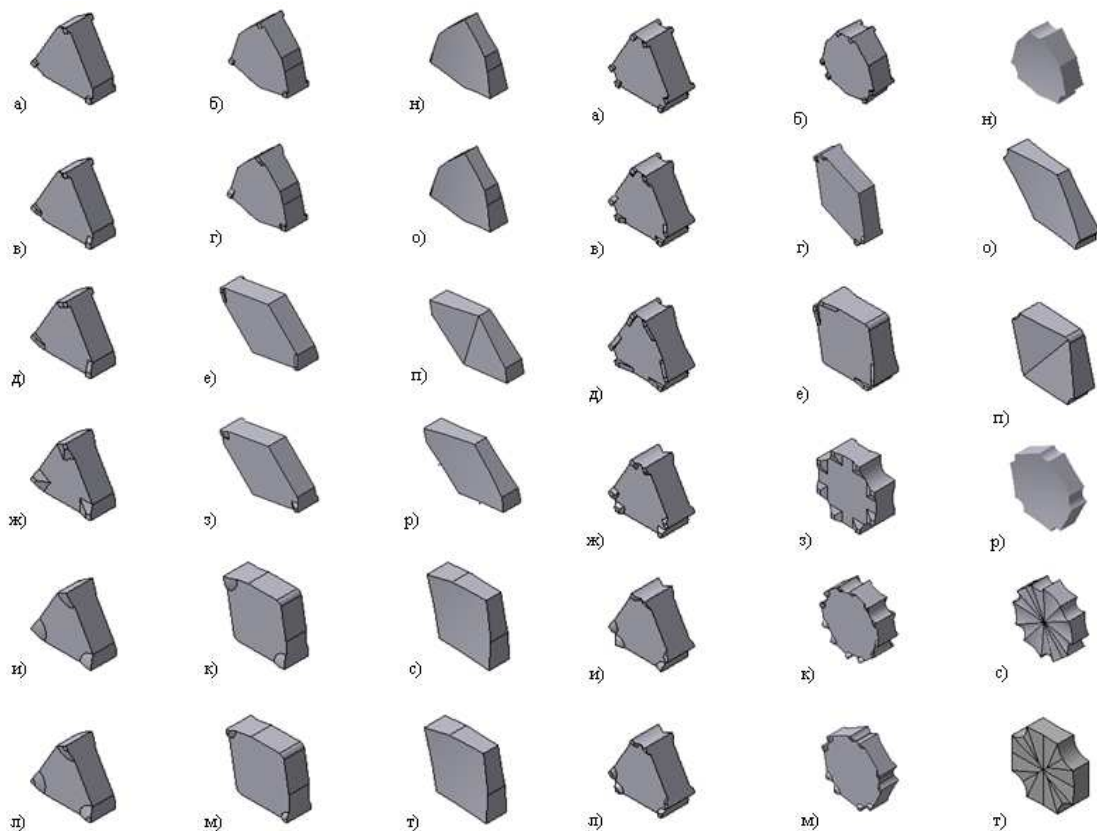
Новые виды неперетачиваемых режущих пластин боковой установки с лысками и выкружками на вершинах для оснащения отрезных резцов
